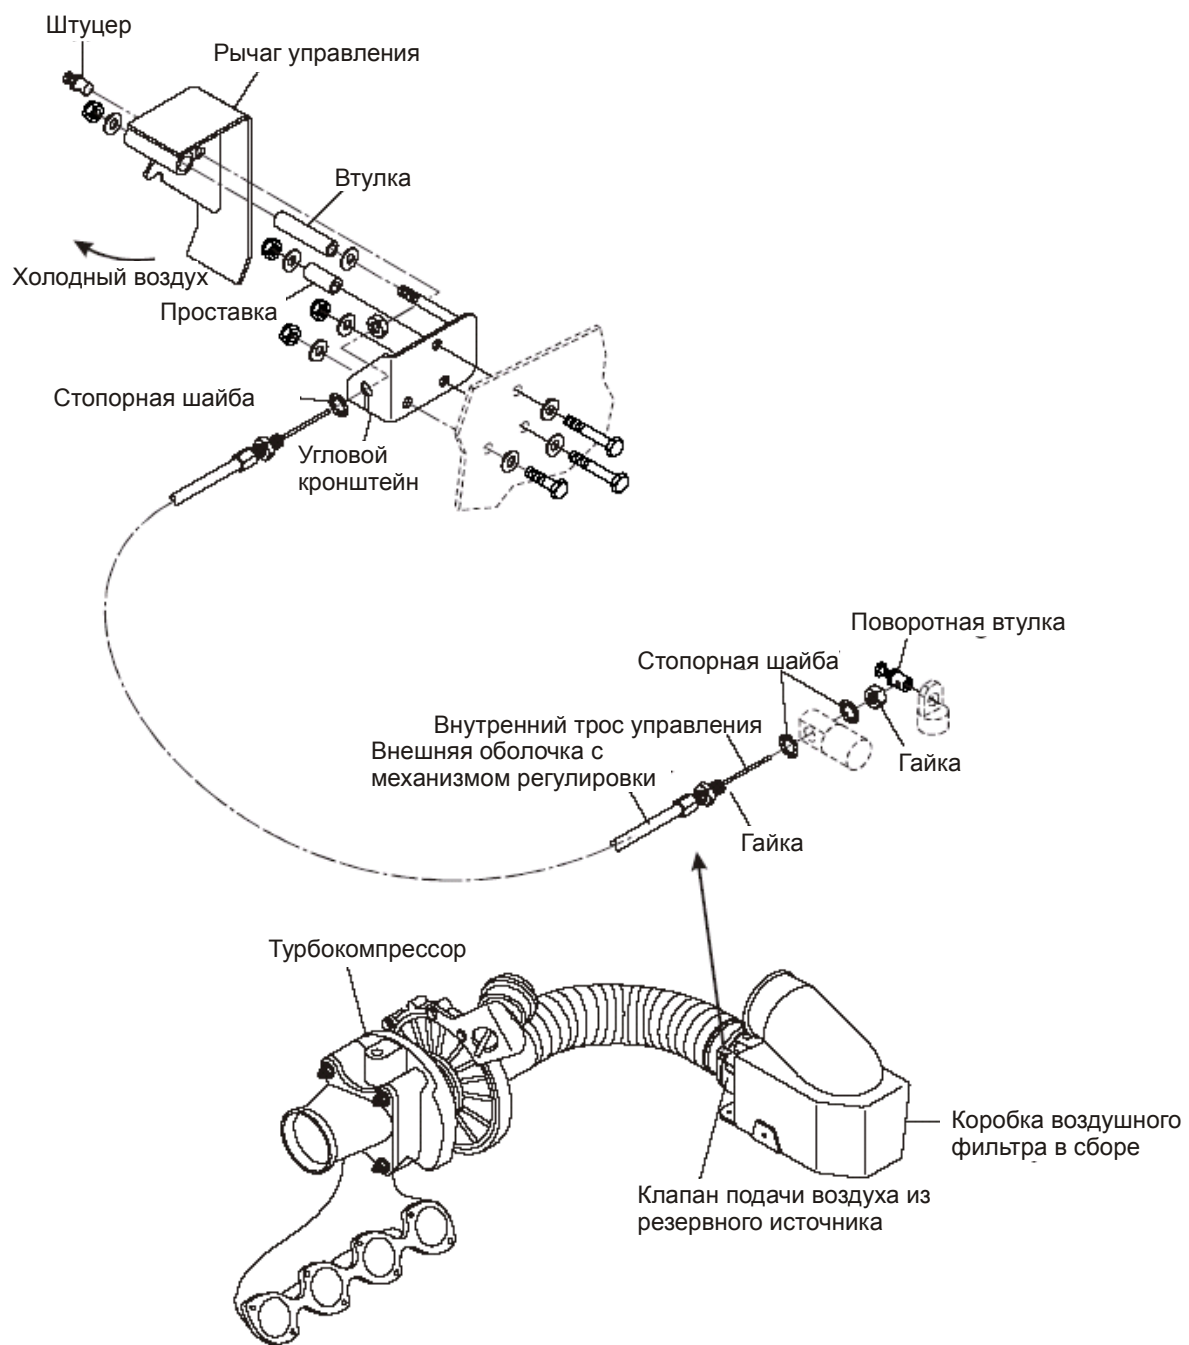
Приводные тросы клапана подачи воздуха из резервного источника
